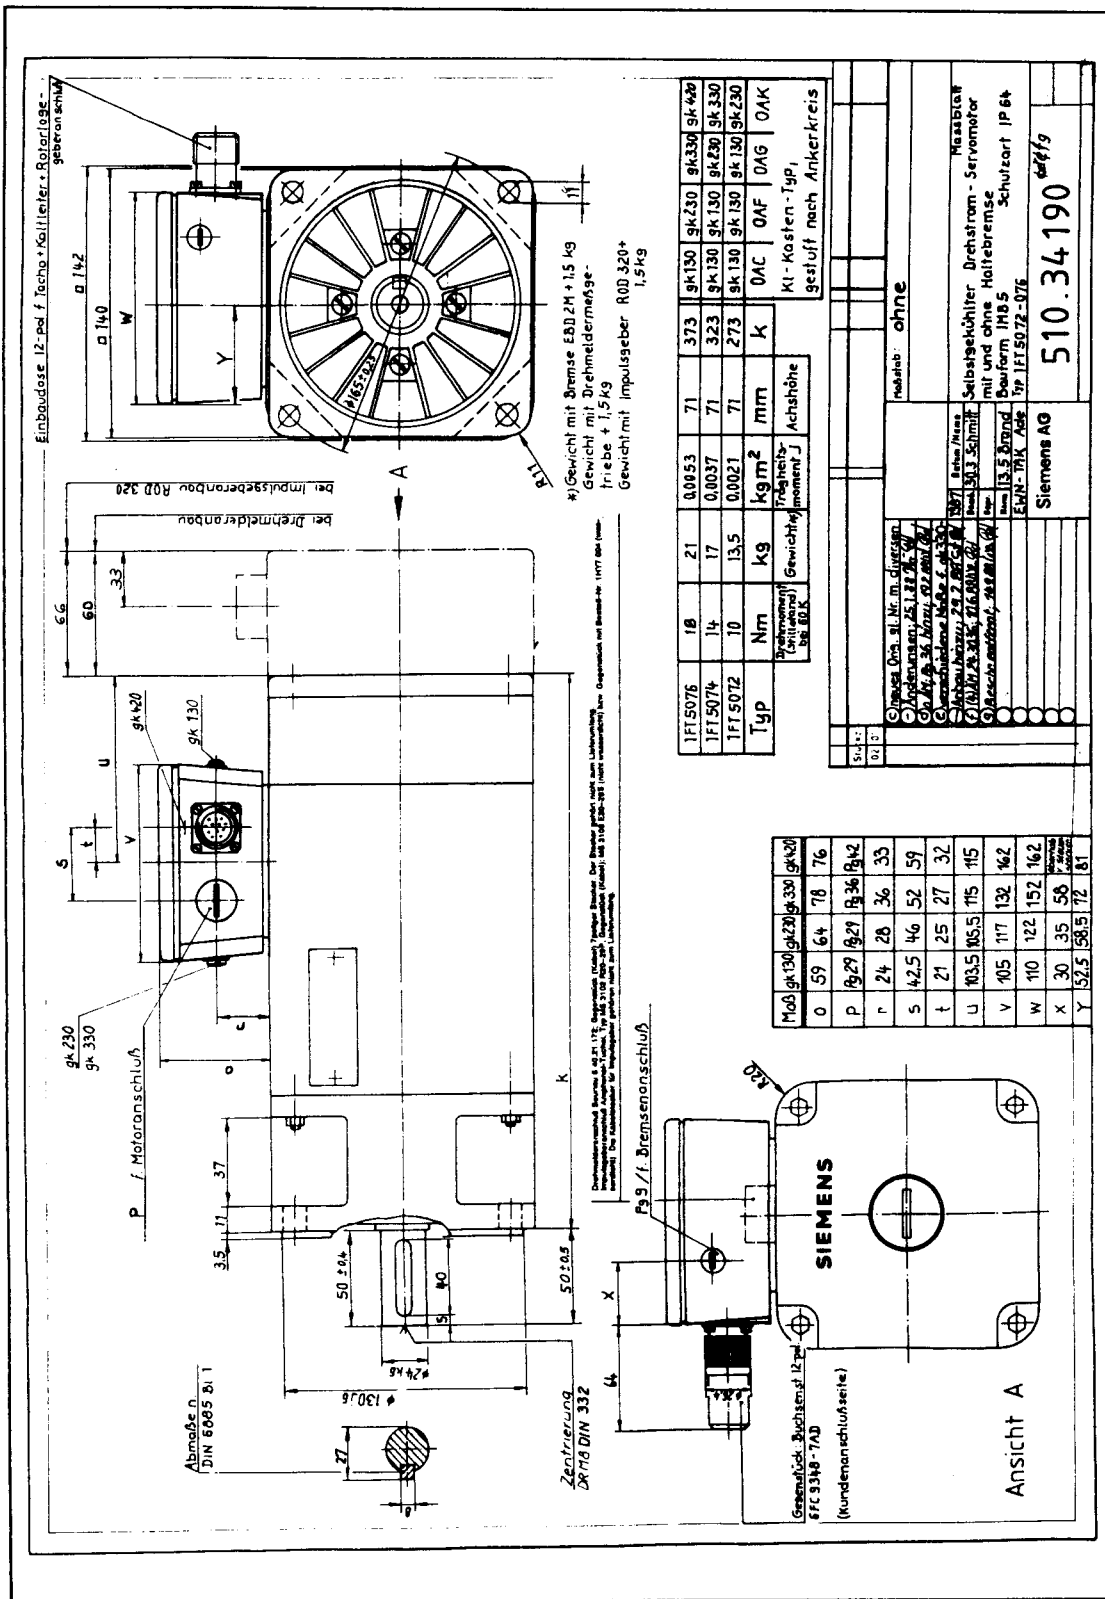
Чертеж серводвигателей переменного тока 1FT5072, 1FT5074 и 1FT5076, конструктивная форма IM B5
